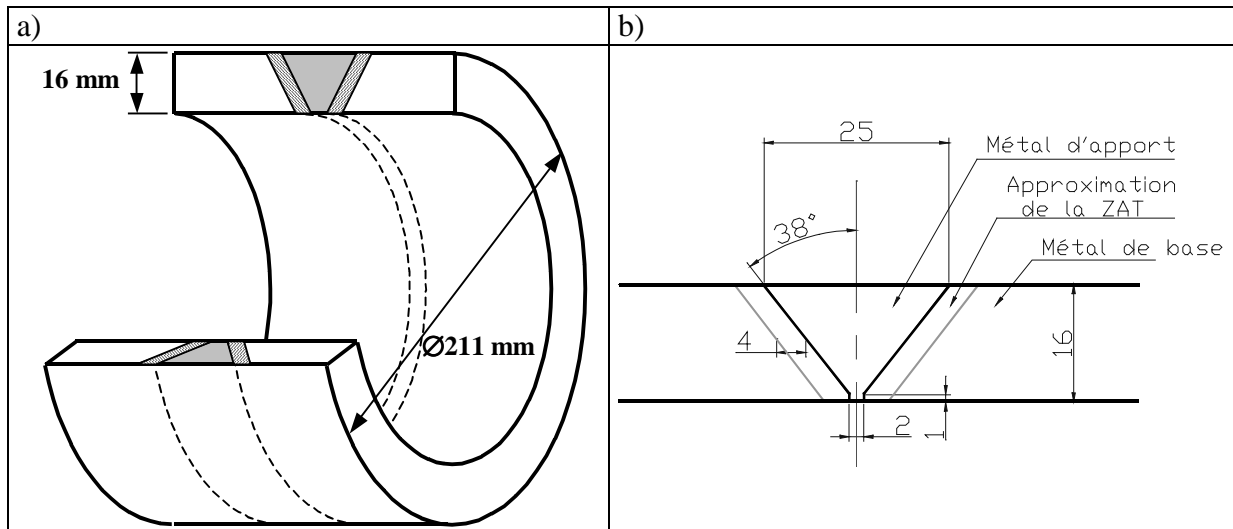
Joints soudés étudiés : a) Joint circconférentiel de raboutement de tube ; b) Géométrie idéalisée de la section du joint.
